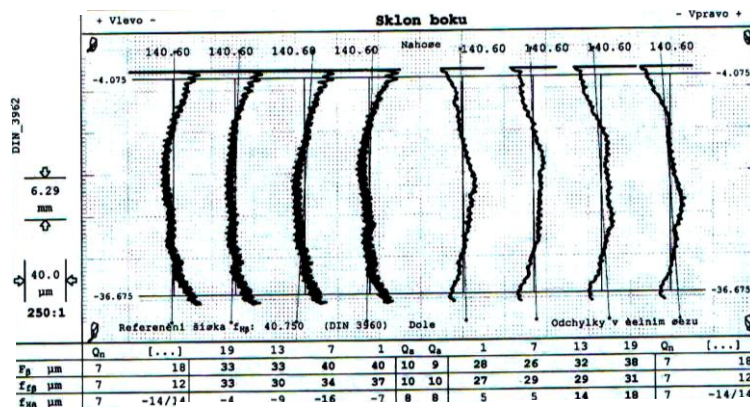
Результаты измерения бочкообразности после зубофрезерования зубчатого колеса 202-1701132-40
